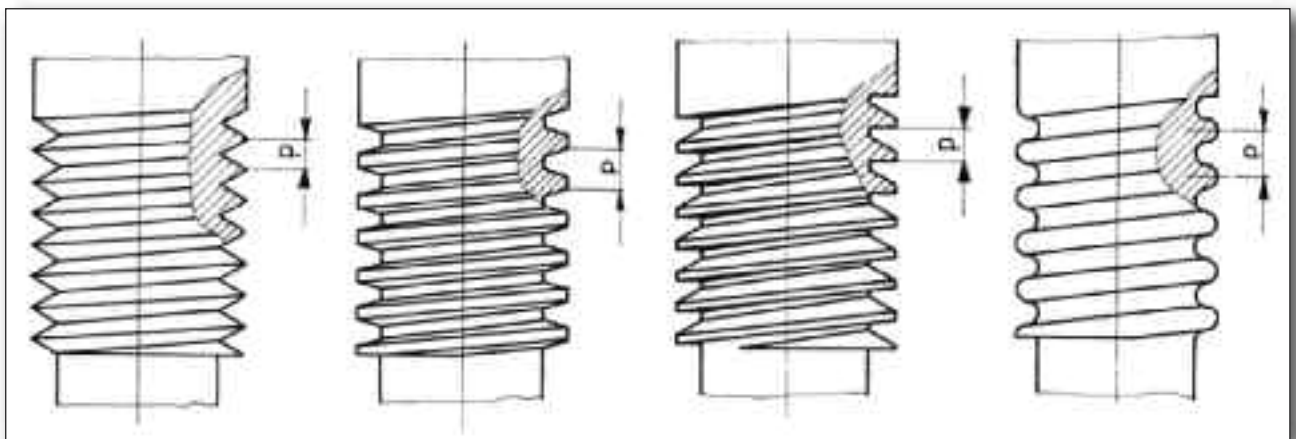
profilo triangolare (Metrica, Whitworth, Gas), viti di collegamento.
